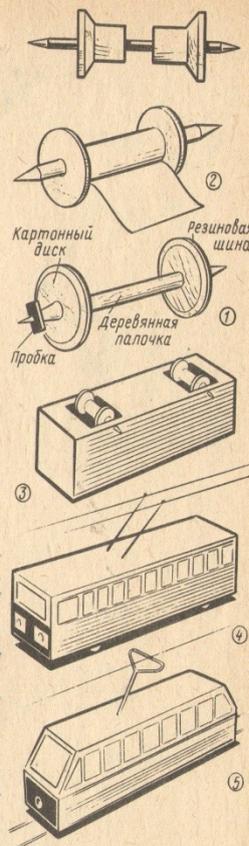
Изготовление моделей из готовых коробок: 1 — изготовление колес; 2 — увеличение длины катушки для колес; 3 — установка колес; 4 — модель троллейбуса; 5 — модель трамвая
